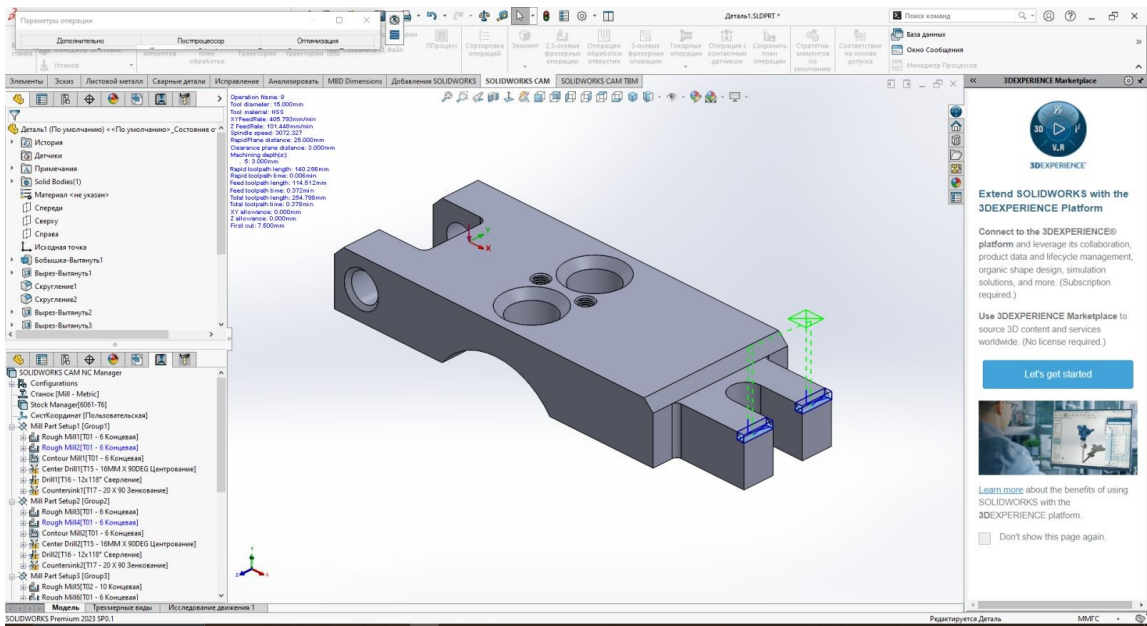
Траекторія обробки - фрезерування фасок
